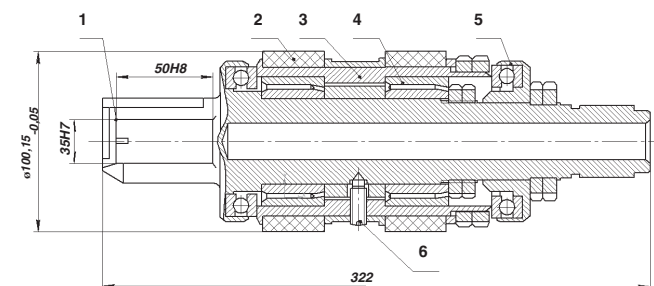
Головка для чистового растачивания с вращающимися направляющими.
